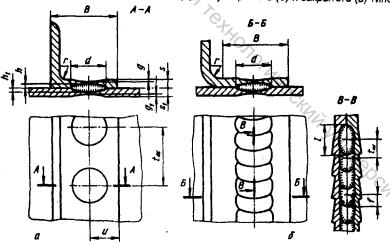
Конструктивные элементы соединений при точечной (а) и щовной (б) сварке
